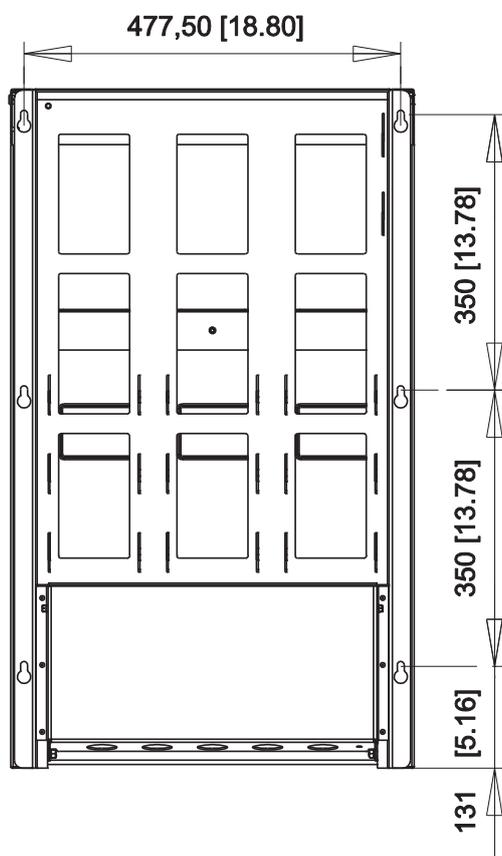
Dimensioni di trapanazione di Sunmaster IS. Tutte le dimensioni sono in mm [pollici]
